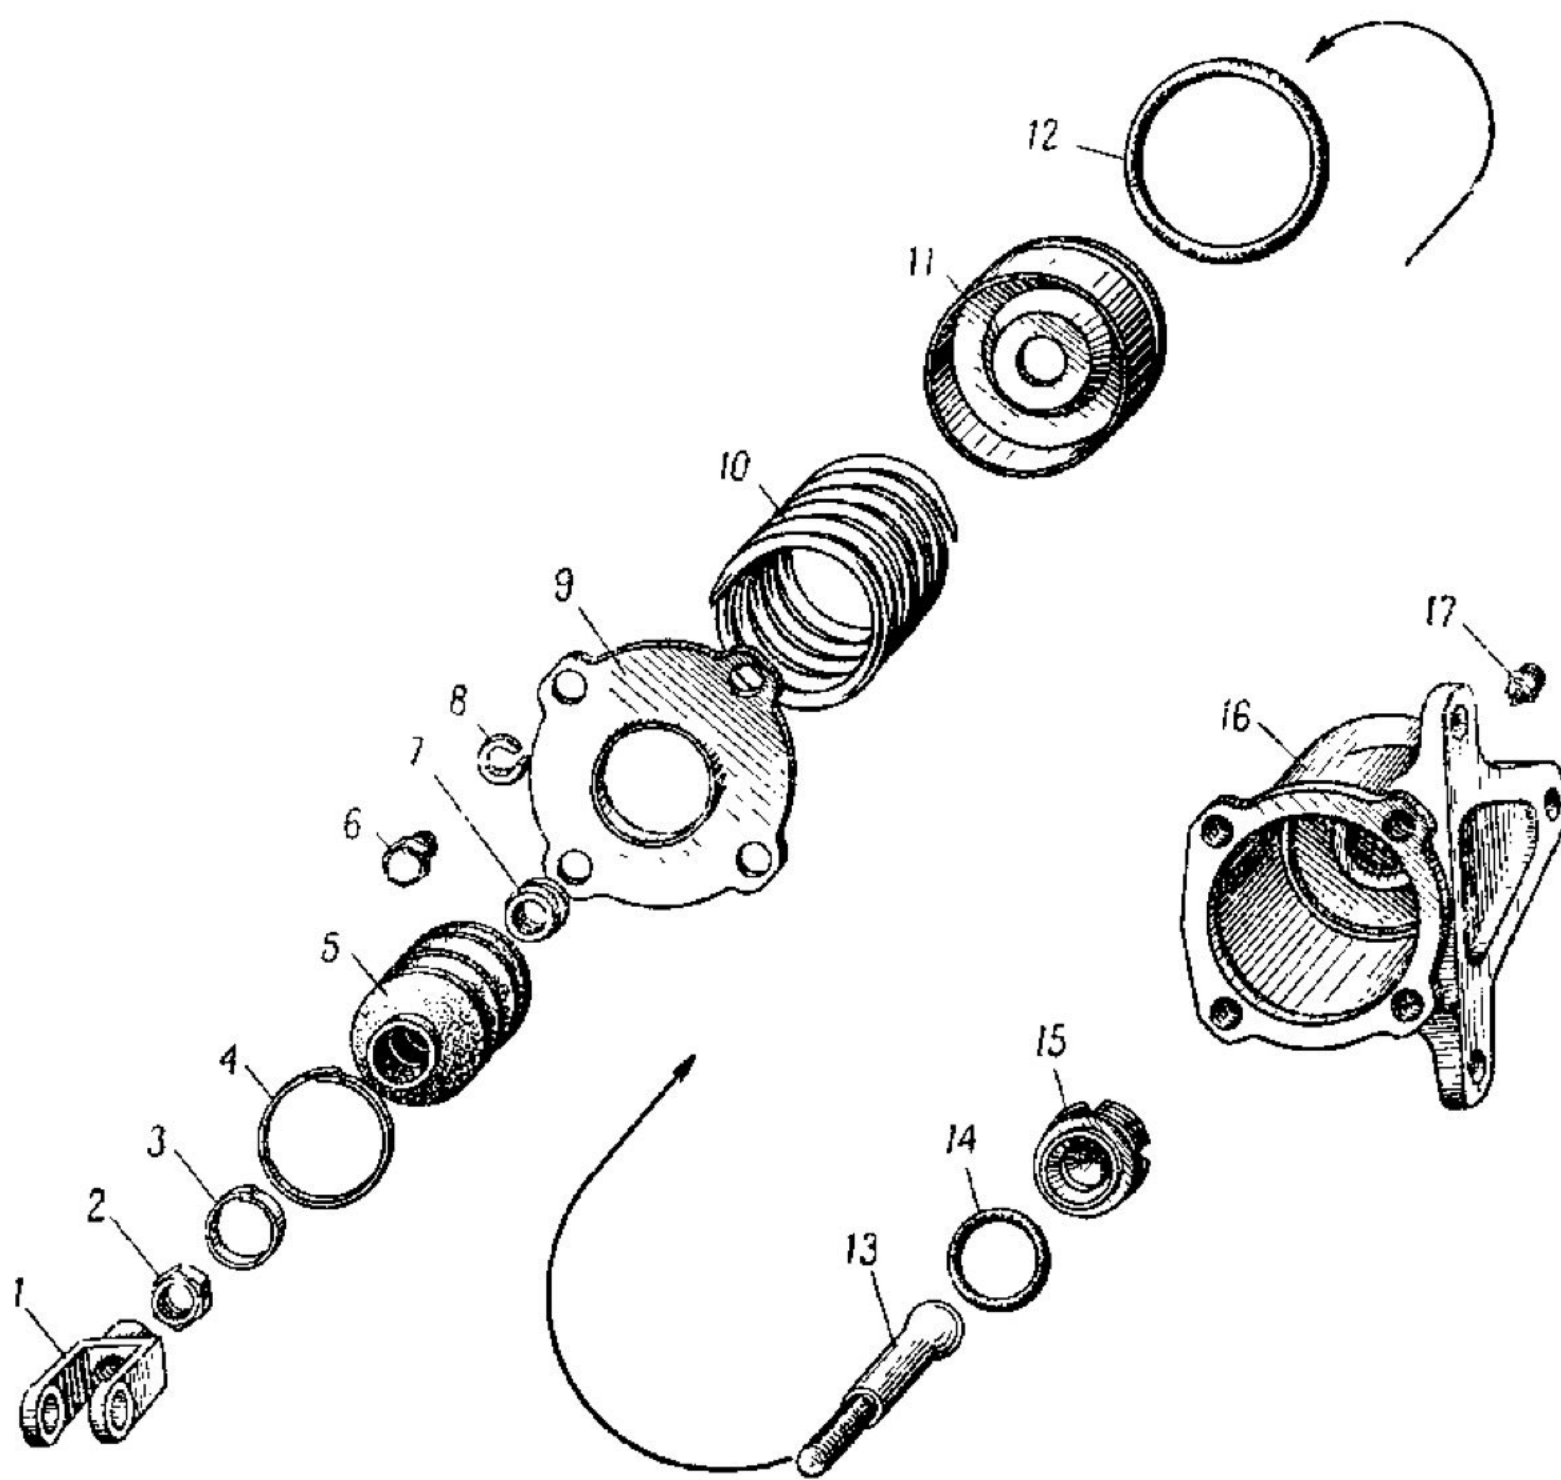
Пневмовыключатель блокировки дифференциала раздаточной коробки
